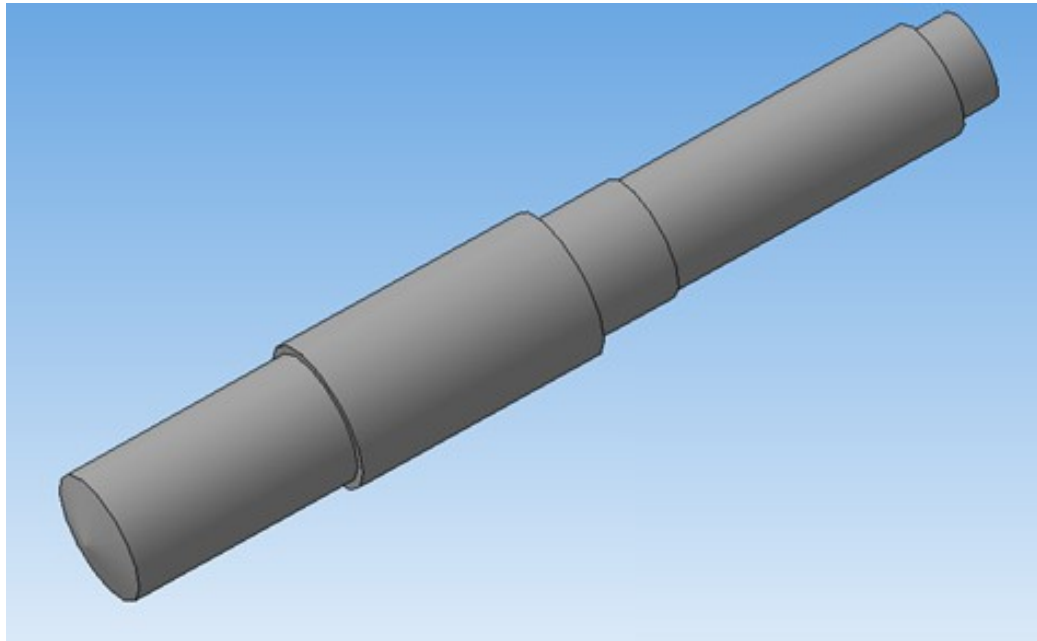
Поковка деталі «Великогабаритний вал $\text{Ø}82 \times 770 \text{ мм}$ »
